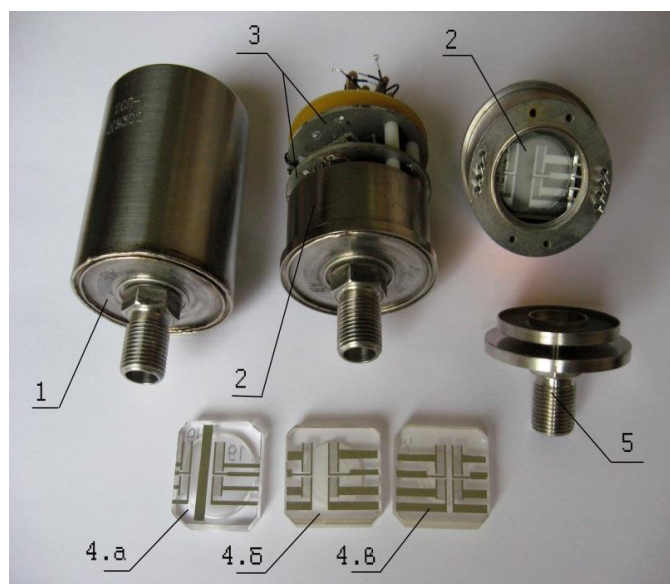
Конструкція АЕП тиску 2SP: 1 – перетворювач у корпусі;
